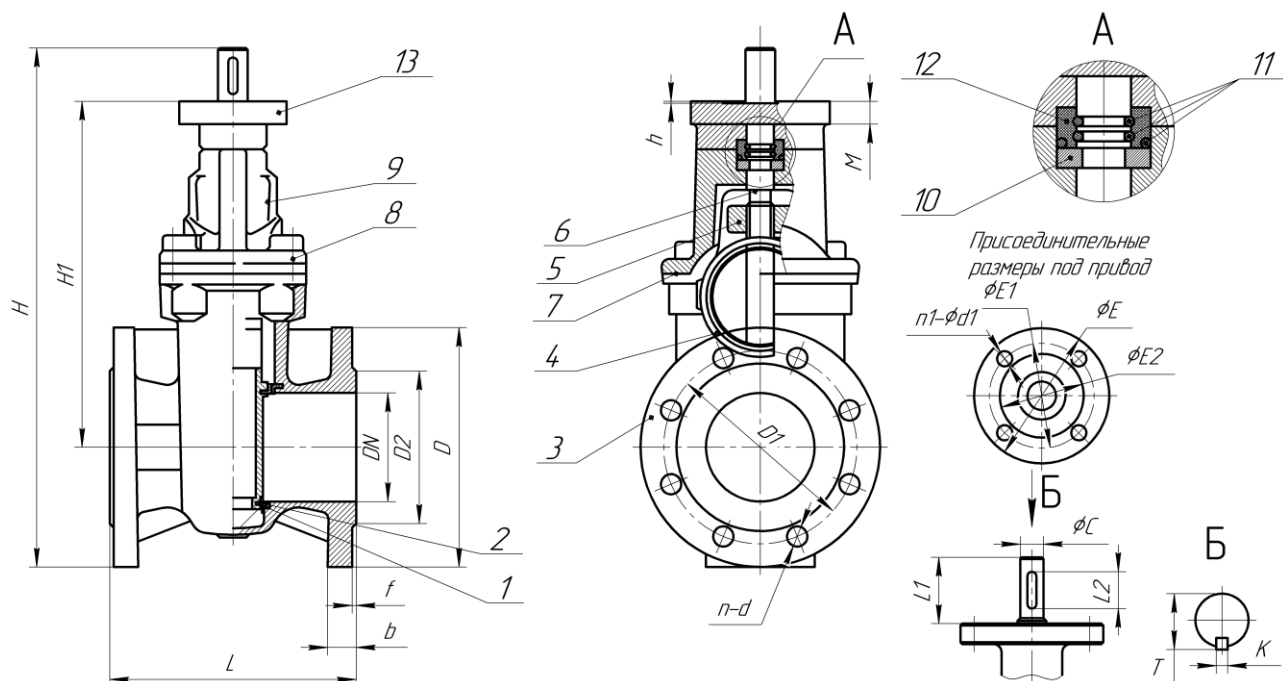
Задвижка без исполнительного механизма DN50-600
